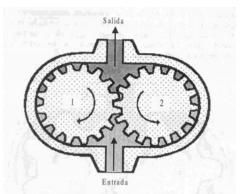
Bomba de engranajes externos de alta presión³⁶
